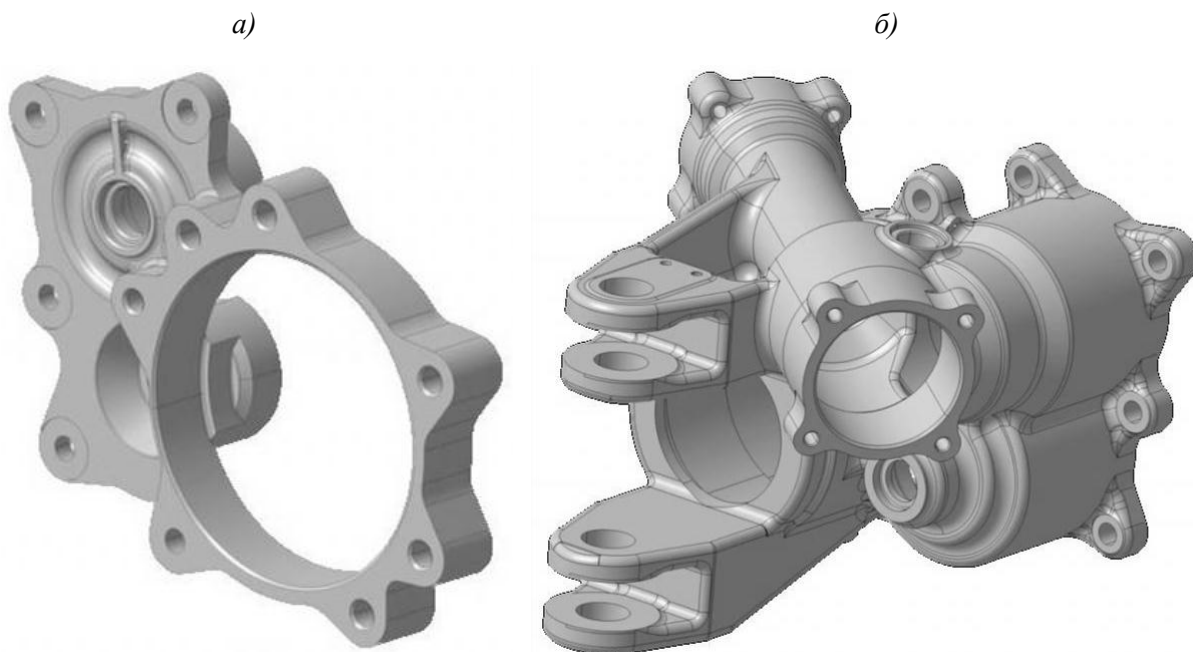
Детали «крышка» (а) и «корпус» (б) подъемника из сплава ВА120
